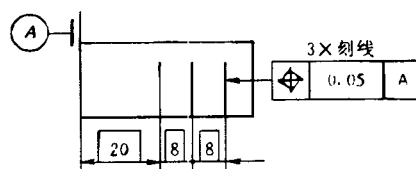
三条刻线有同一位置度公差带要求的简化标注
